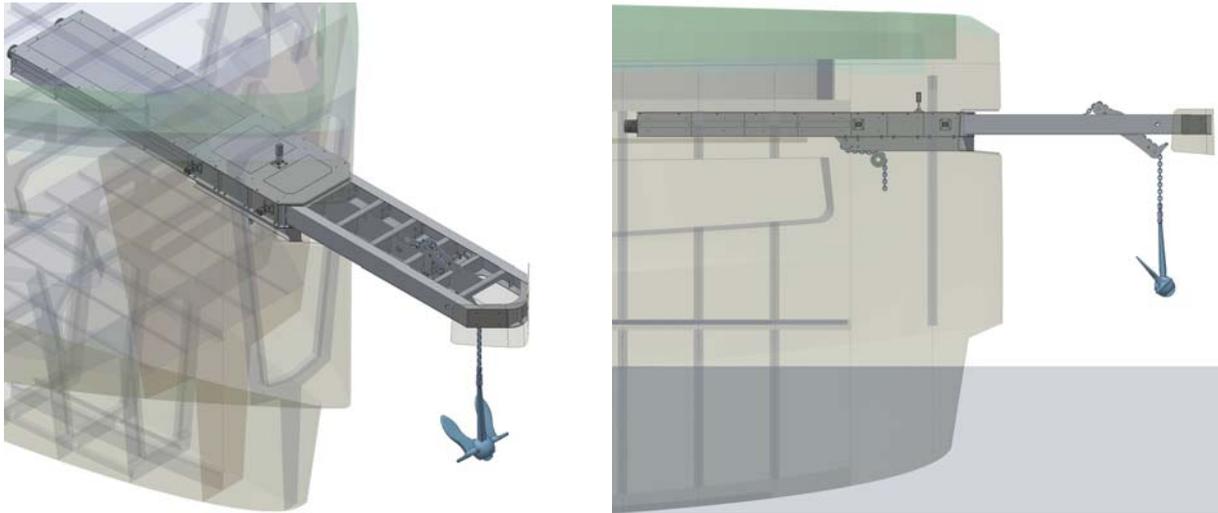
Im Bug eingebaute Ankerlade mit ausgefahrener Lade, transparente Darstellung
